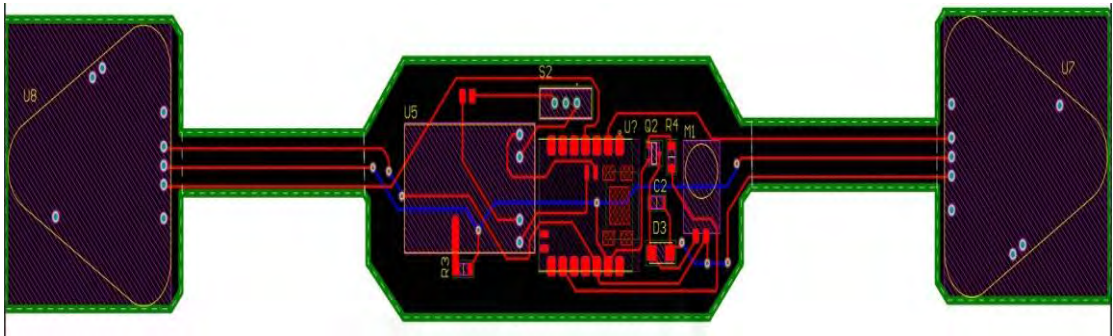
Vista superior de la tarjeta electrónica PCB
